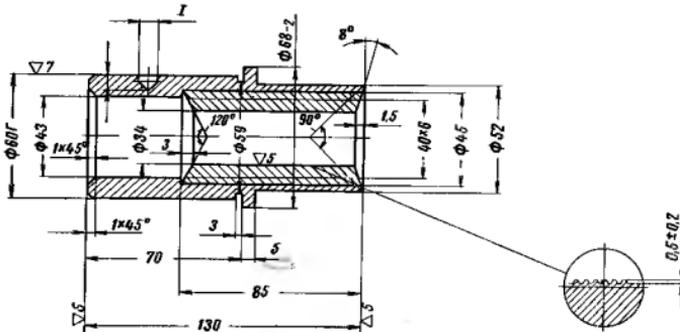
Гайка биметаллическая. Деталь 6М82-6-21А
